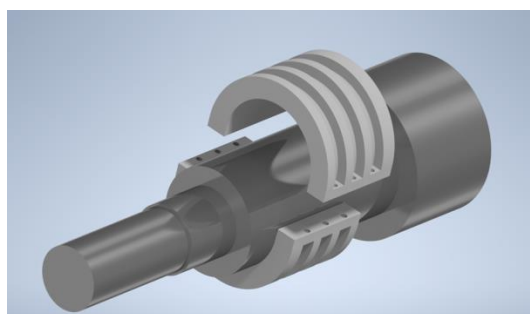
Соединение кулачкового вала и вала мотор-редуктора
